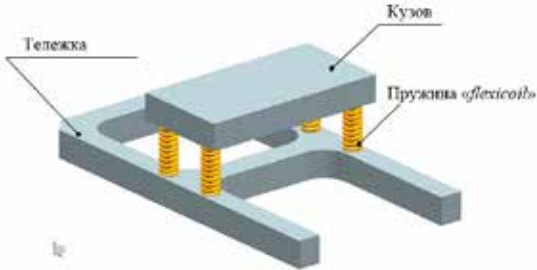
3D-модель конструкции кузовного рессорного подвешивания электровоза 2ЭС6 [выполнено авторами].
